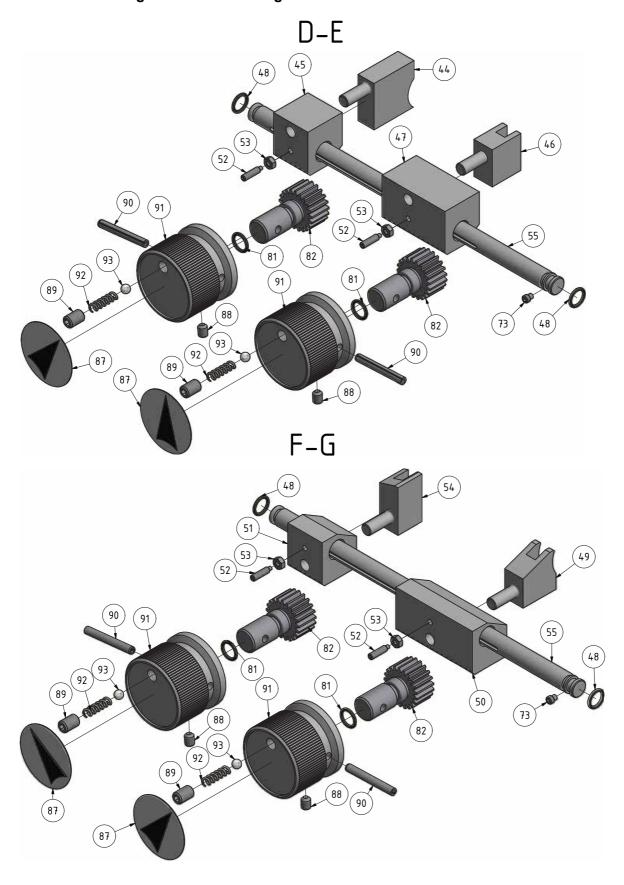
Vorschubgetriebe 6-6 - Feed gear 6-6
